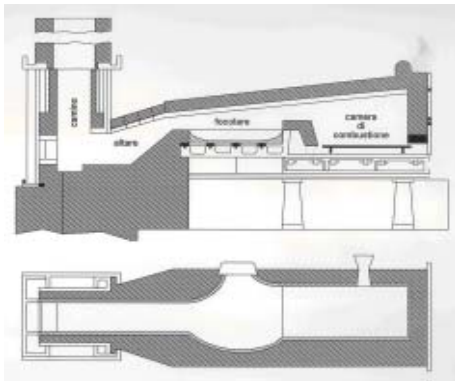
Pianta e sezione schematica di un forno a pudellare
